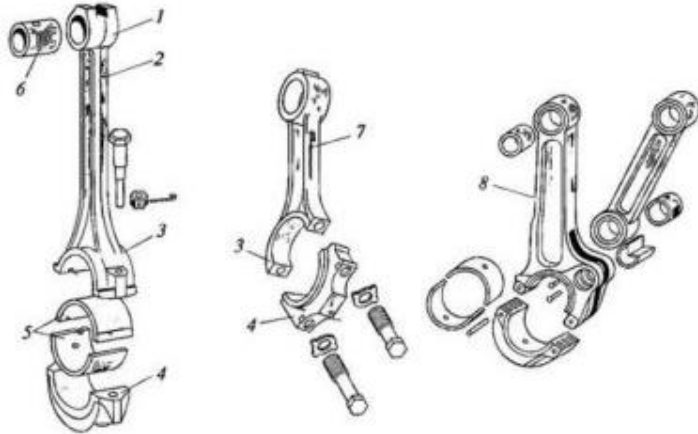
Деталі шатунної групи: 1- верхня головка шатуна; 2 – стержень; нижня головка шатуна; 4 – кришка нижньої головки ; 5 – вкладні; 6 – втулка; 7 – шатун дизеля; 8 – основа шатунного вузла.
